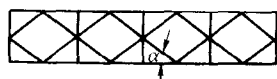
焊接桁架在工程上的应用示例
